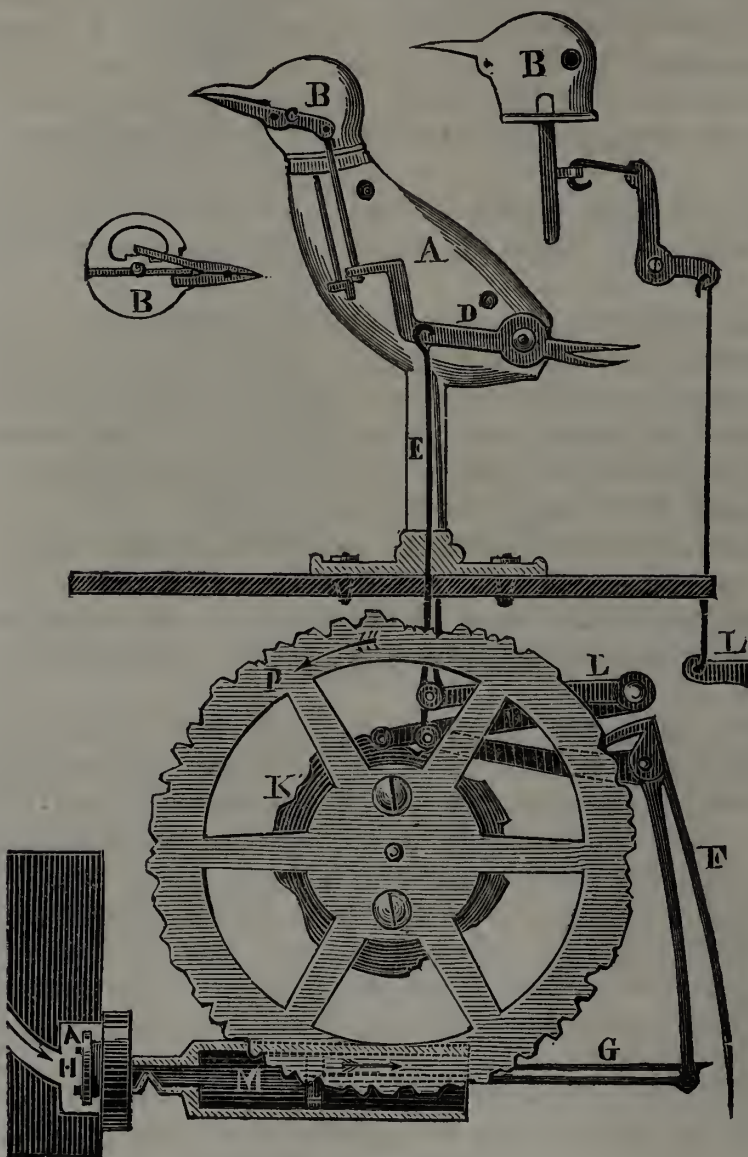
Oiseau chantant. — A, corps de l'oiseau; — B, tête vue de plusieurs côtés; — C, bec; — D, levier destiné à mouvoir le bec; — E, fil métallique correspondant au levier F qui frappe la tige G; — H, soupape du sifflet; — I, levier destiné à transmettre le mouvement au piston R dans le sifflet M; — K, roue qui fait mouvoir les leviers F et L; — N, chambre d'air; — O, soufflet.
